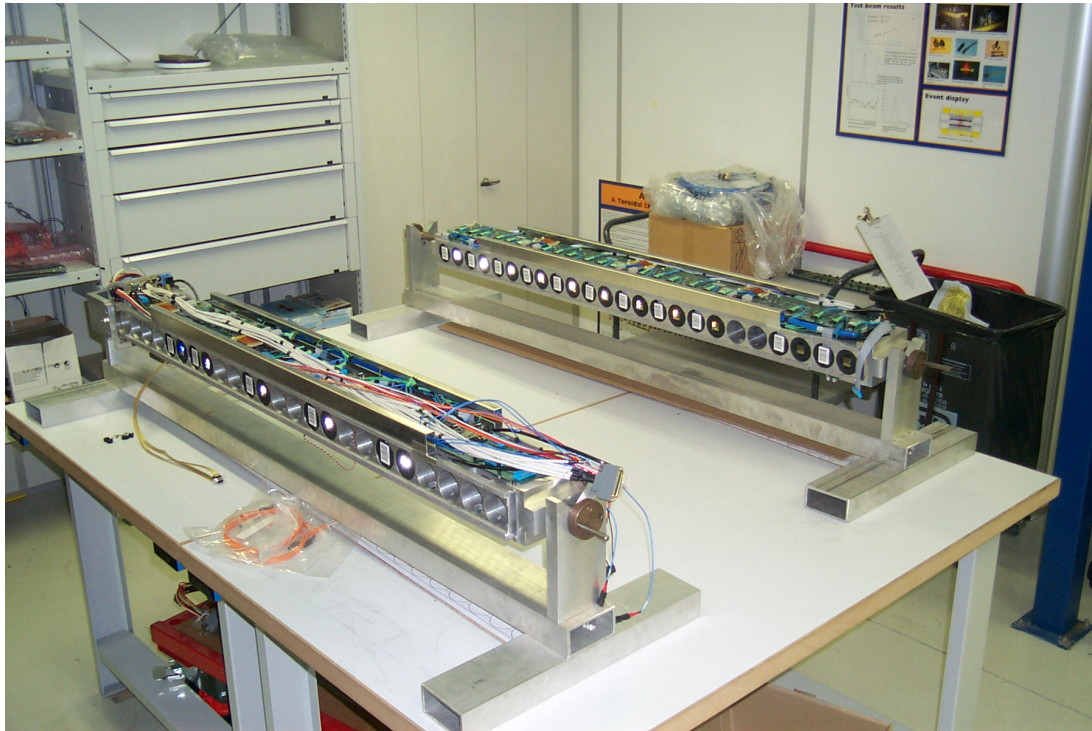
Photo des deux lignes de production. Au premier plan, un tiroir externe en cours d'assemblage, au second plan, un tiroir interne équipé.
